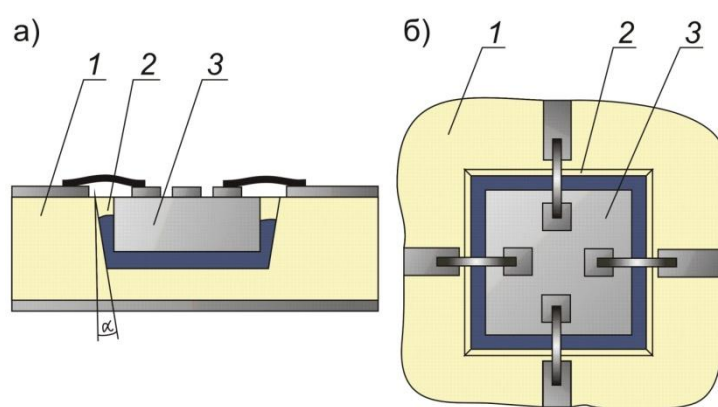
Монтаж бескорпусного кристалла в углубление, полученное прецизионным лазерным фрезерованием [2]; а) разрез и б) вид сверху: 1 – подложка, 2 – углубление, 3 – кристалл
